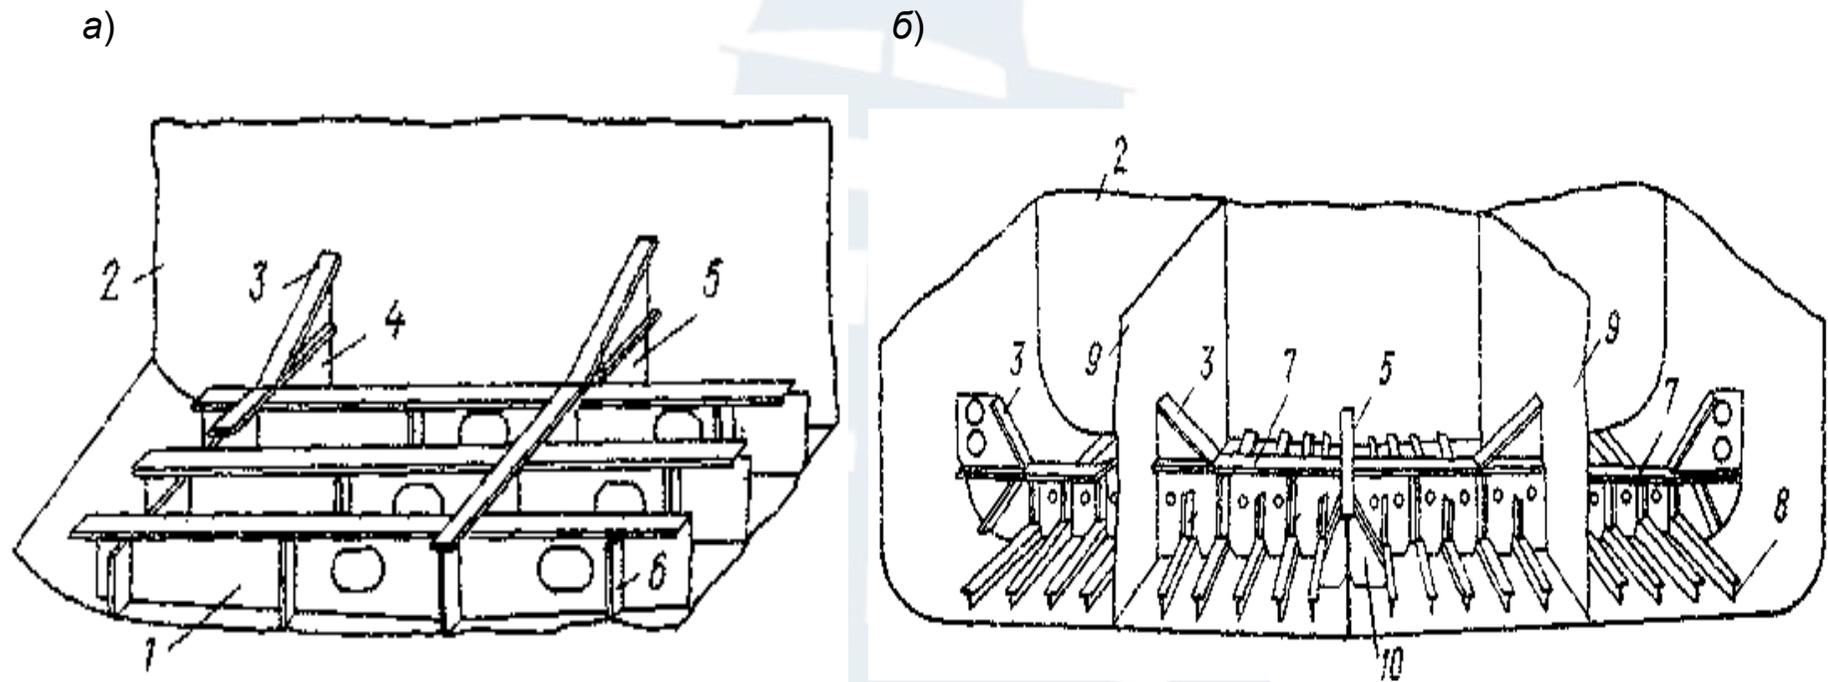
Конструкция днищевого перекрытия без двойного дна:
